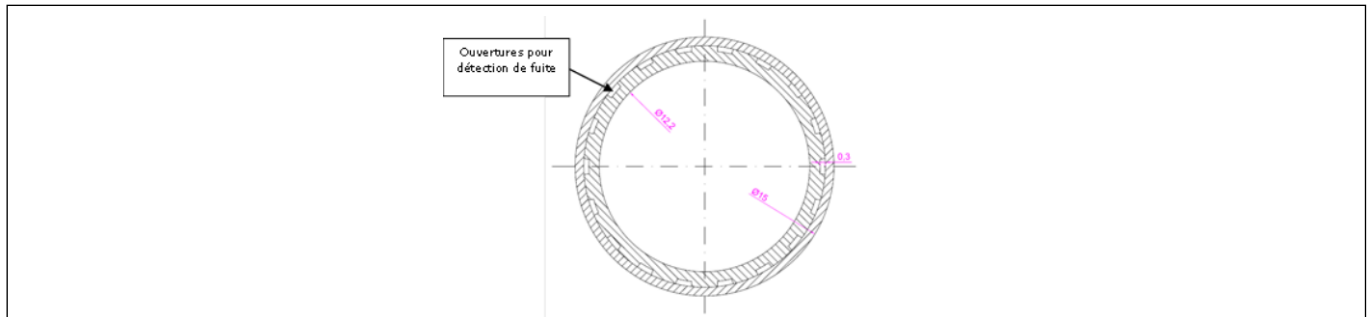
Coupe serpentin échangeur double paroi du ReQup®-Floor
